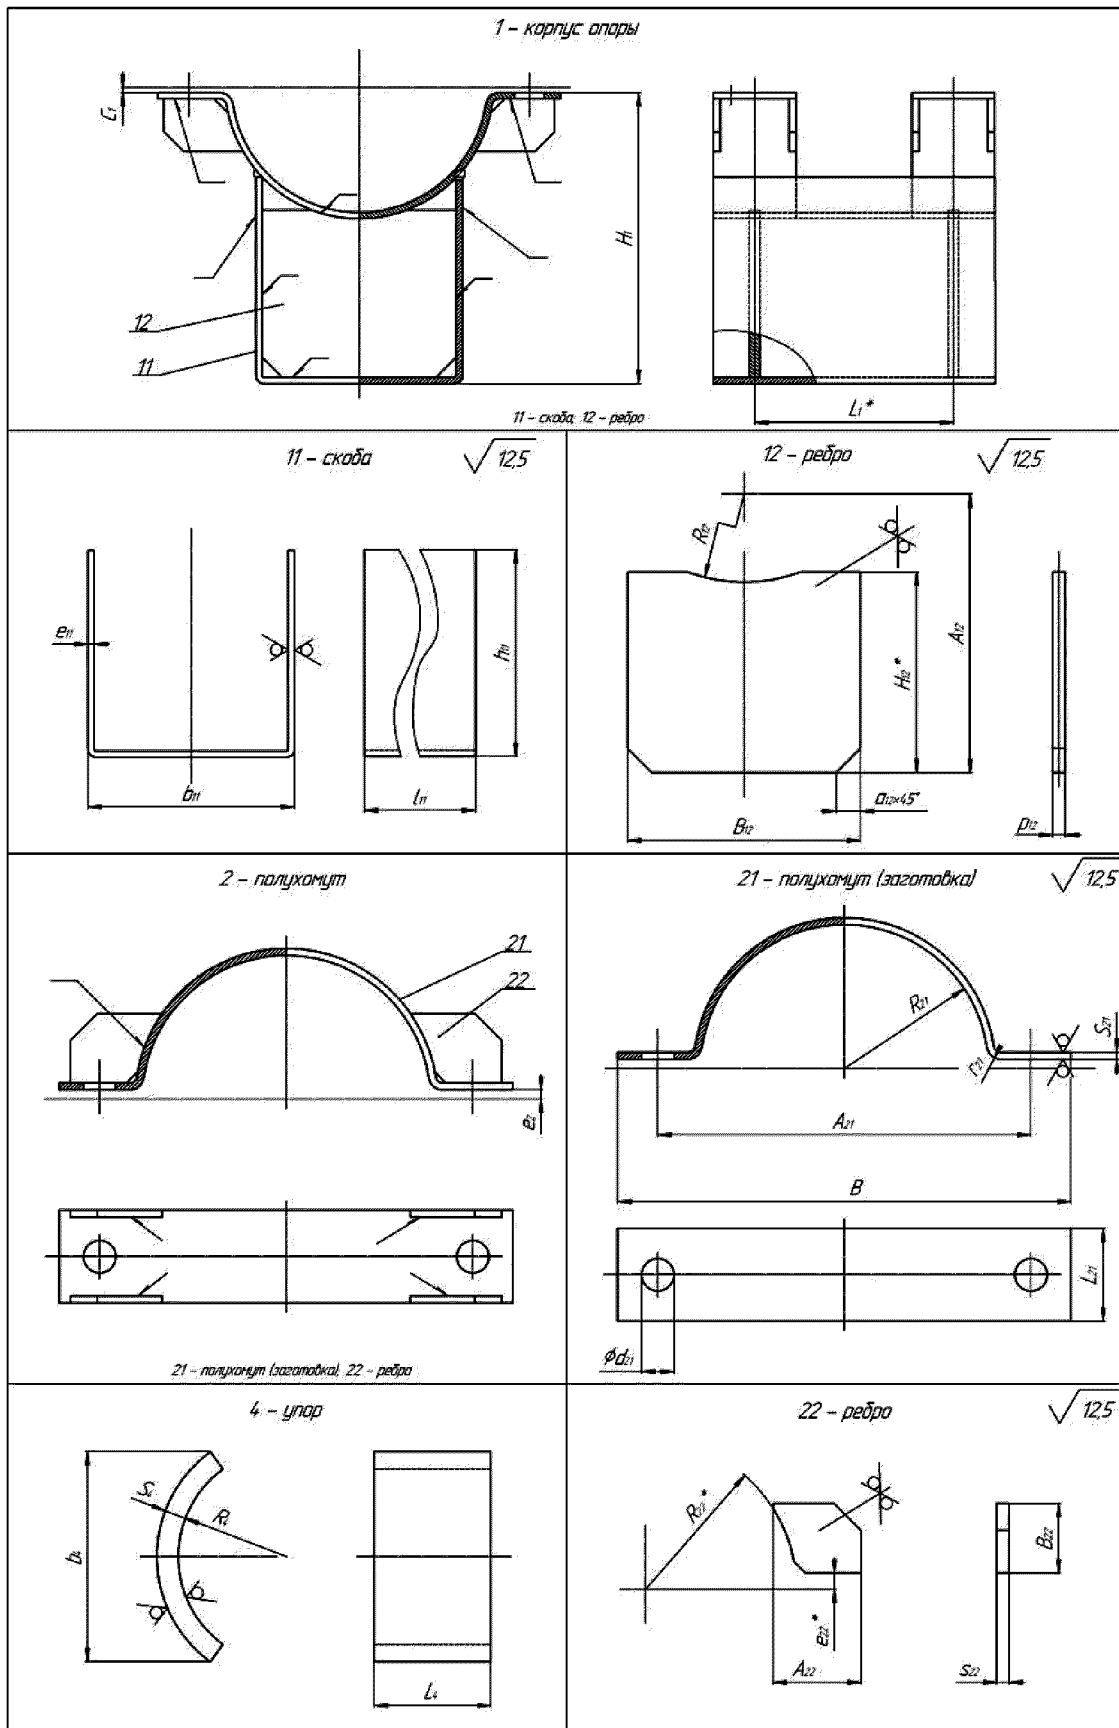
Детали изделий 01-XXXX-F-1C-03-A,
